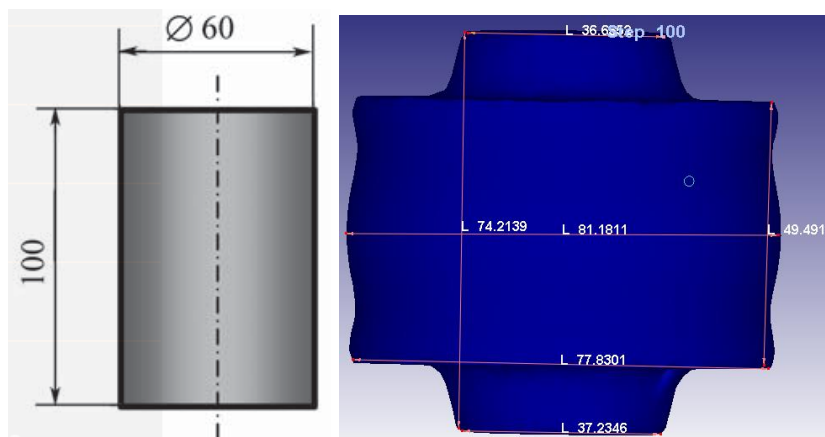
Вигляд початкової заготовки та кінцевої заготовки
